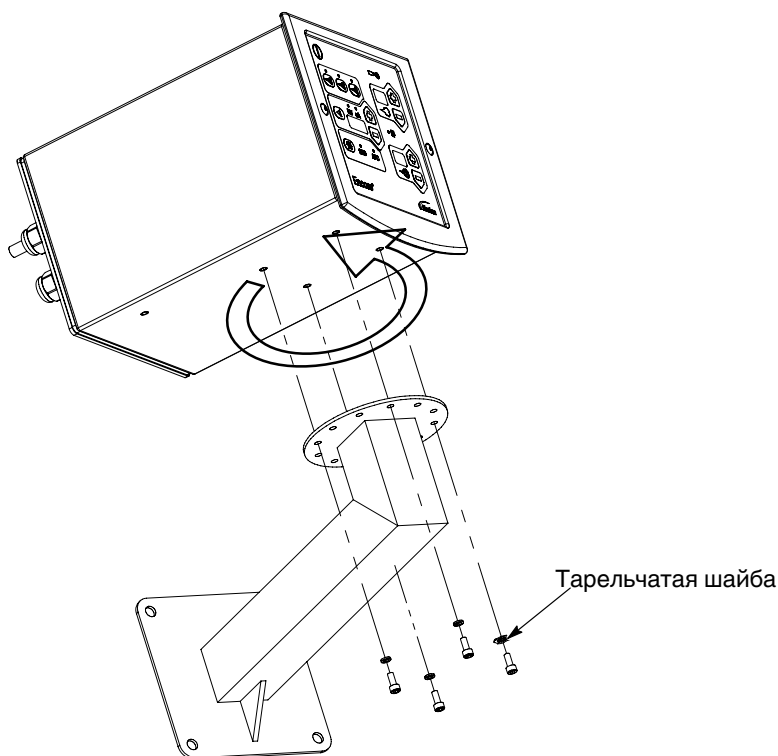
Монтаж кронштейна для монтажа на стене
